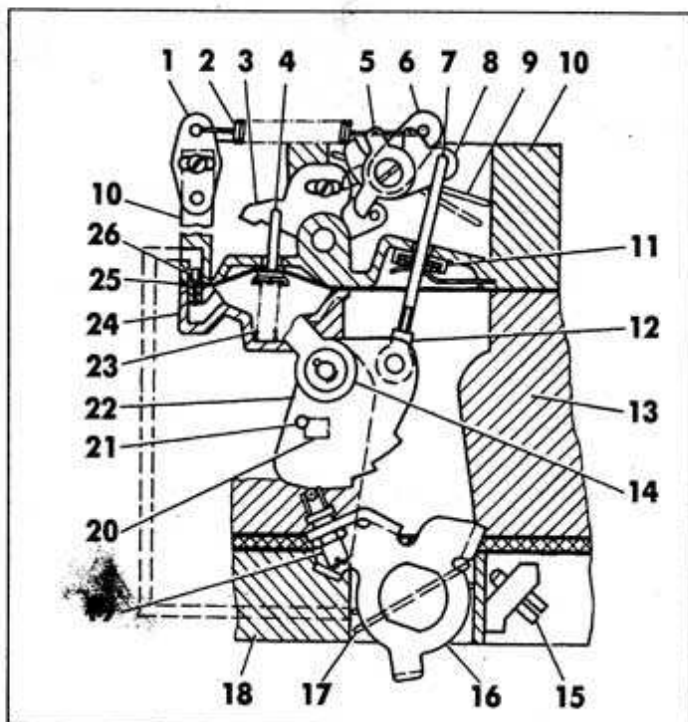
Схема полуавтоматического устройства пуска и прогрева: 1, 5, 6 и 16 – рычаги; 2 – пусковая пружина; 3 – промежуточный рычаг; 4 – тяга пневмокорректора; 7 – тяга; 8 – секторный рычаг; 9 – воздушная заслонка; 10 – крышка карбюратора; 11 – уплотнительный элемент; 12 – регулировочная муфта; 13 – корпус поплавковой камеры; 14 – рычаг привода воздушной заслонки; 15 – упорный винт дроссельной заслонки первичной секции карбюратора; 17 – дроссельная заслонка первичной секции карбюратора; 18 – корпус смесительных камер; 19 – винт с роликом; 20 – упор; 21 – штифт; 22 – профильный рычаг; 23 – пружина пневмокорректора; 25 – диафрагма; 26 – жиклер пневмокорректора
